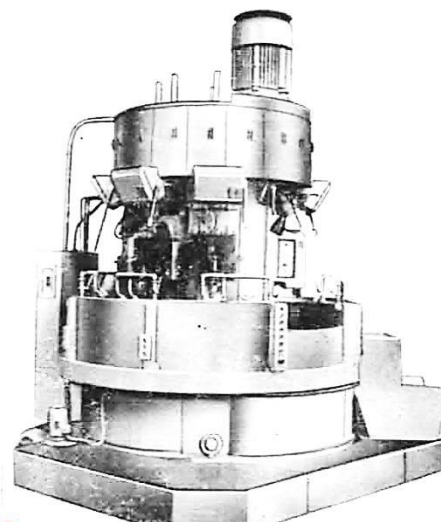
1К282 Станок токарный вертикальный полуавтомат
